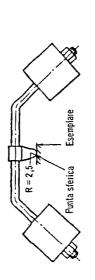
Dispositivo di fissaggio dei portalampade per la prova d'urto Dimensioni in mm
